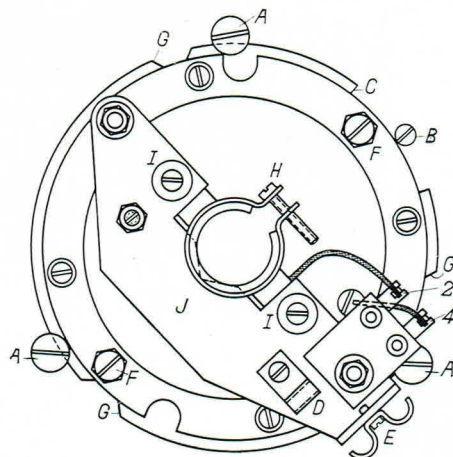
Disposition des vis sur la partie arrière et ensemble des bobines.
